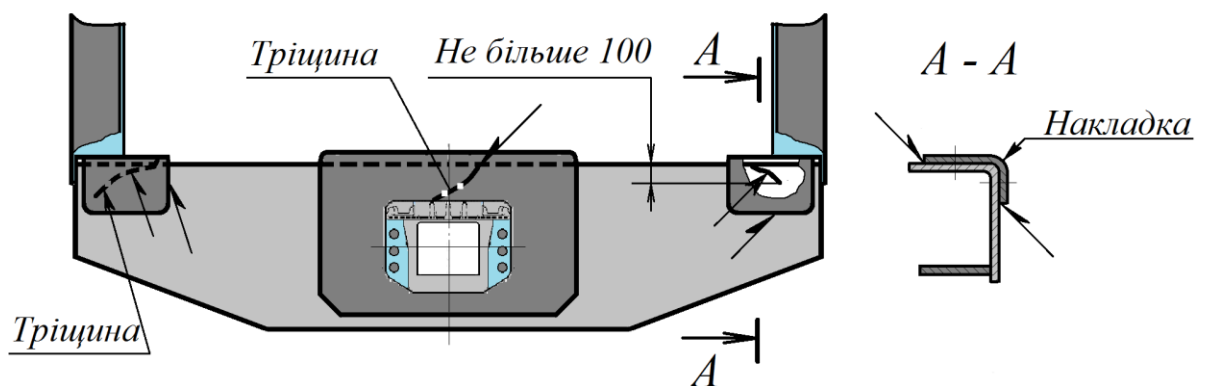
Балка напіввагона з металевою обшивкою, яка відремонтована зварюванням
